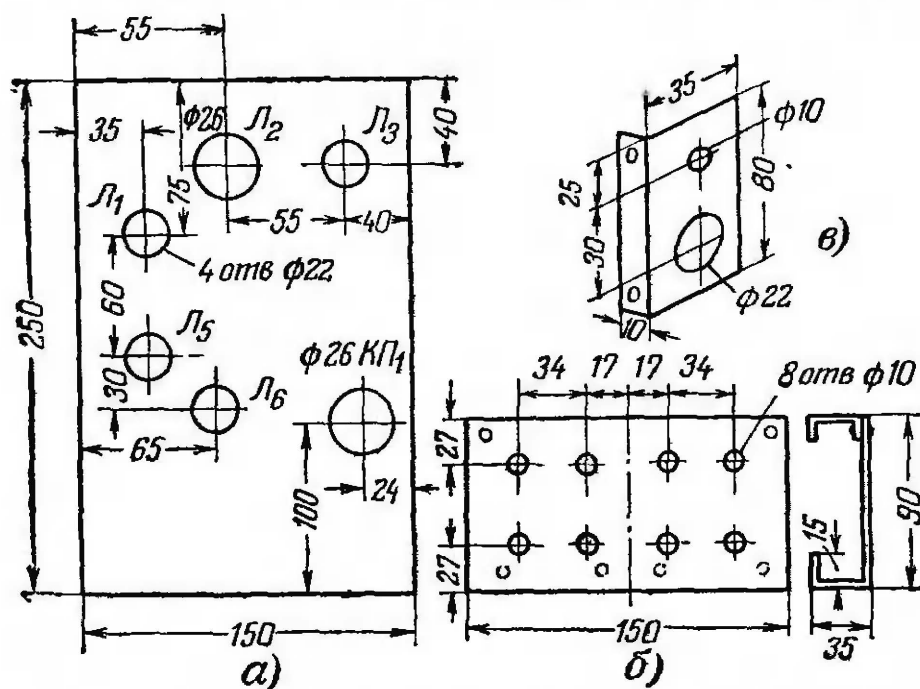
Детали шасси блока развертки для кинескопа 35ЛК2Б.
